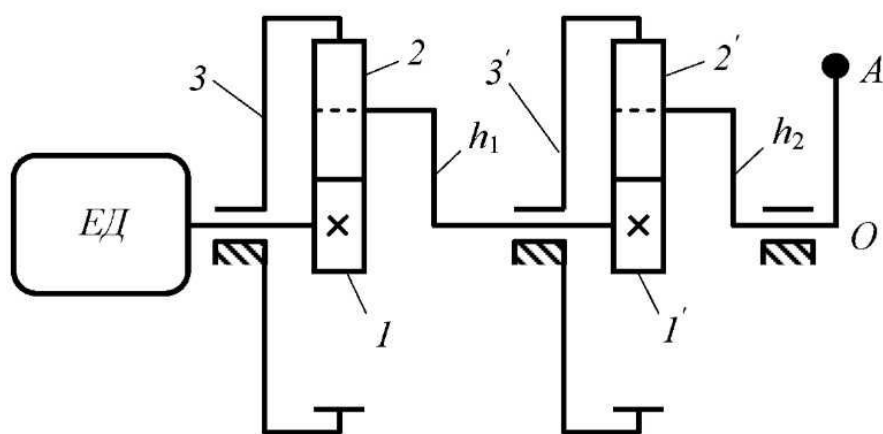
Принятая кинематическая схема зубчатого редуктора привода входного звена шарнирного механизма
